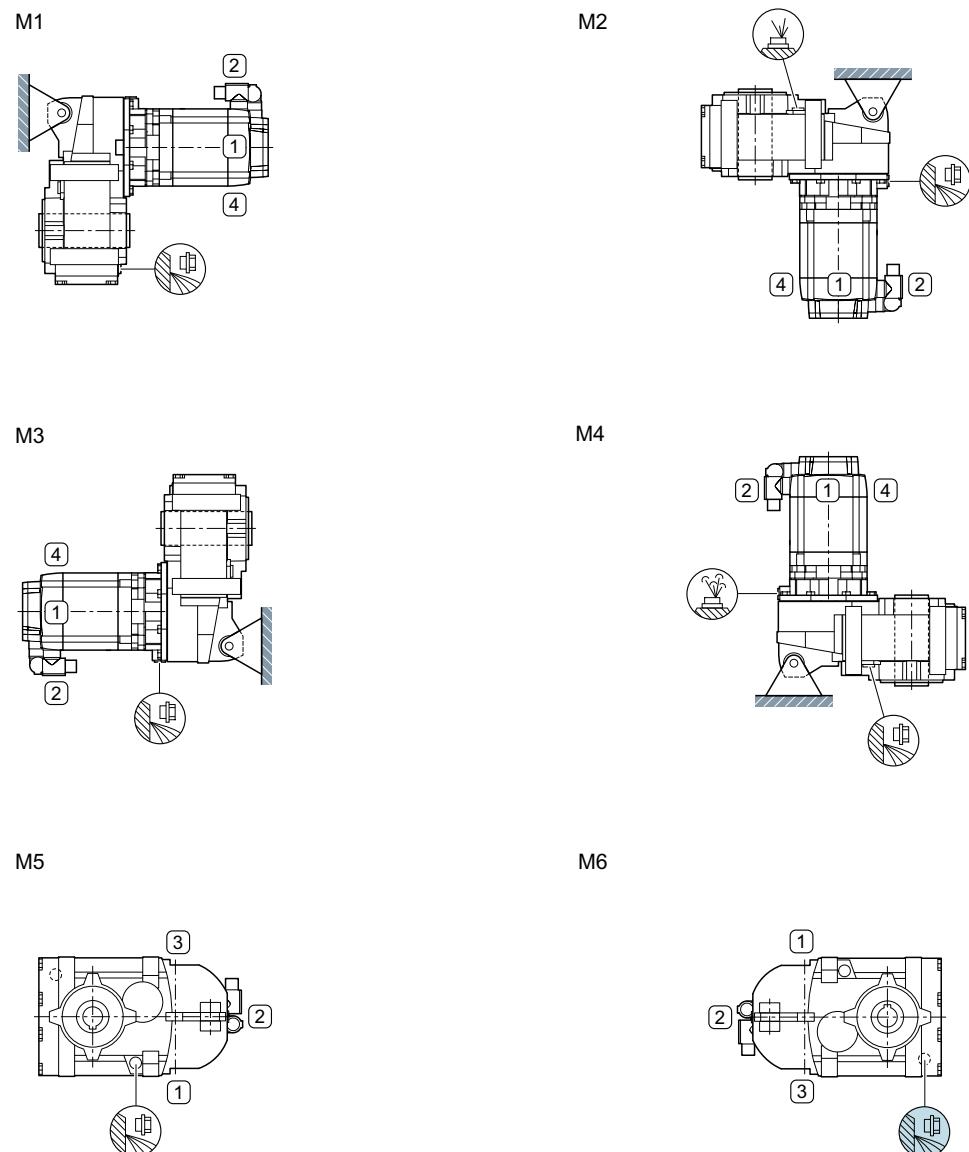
Einbaulagen für Servo-Flachgetriebemotoren FZAD und FDAD, Aufsteckausführung, Baugrößen 29, 2-stufig und 3-stufig
